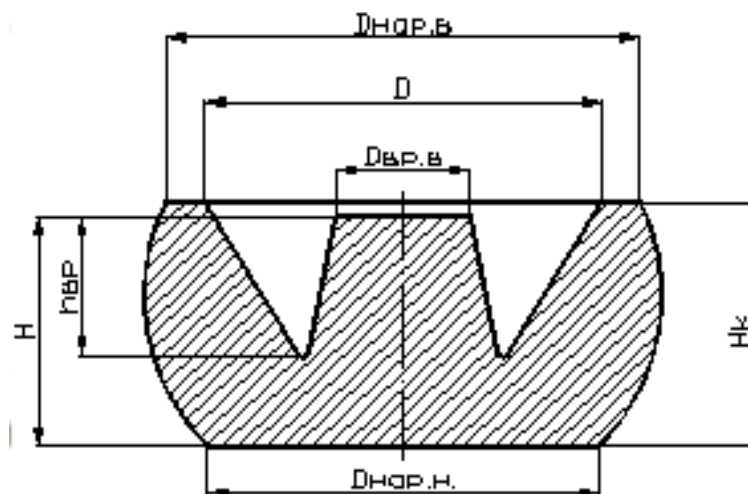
Форма заготовки після впровадження кільцевого конусного інструменту
